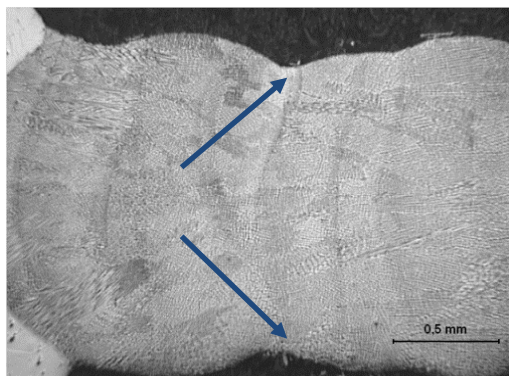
Detalle de la sección transversal del cierre de cuchillas soldado F (5 ipm)
